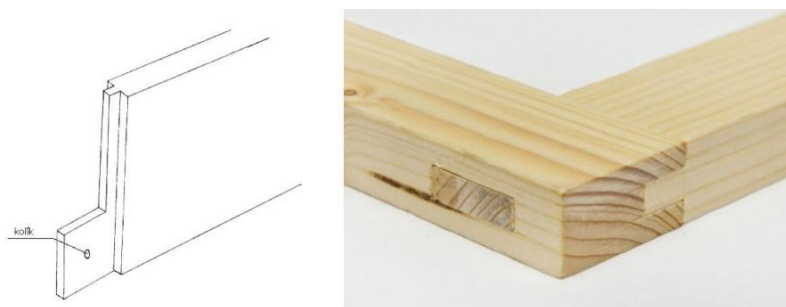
, Obr. 84. a Obr. 85. Svlakový spoj
